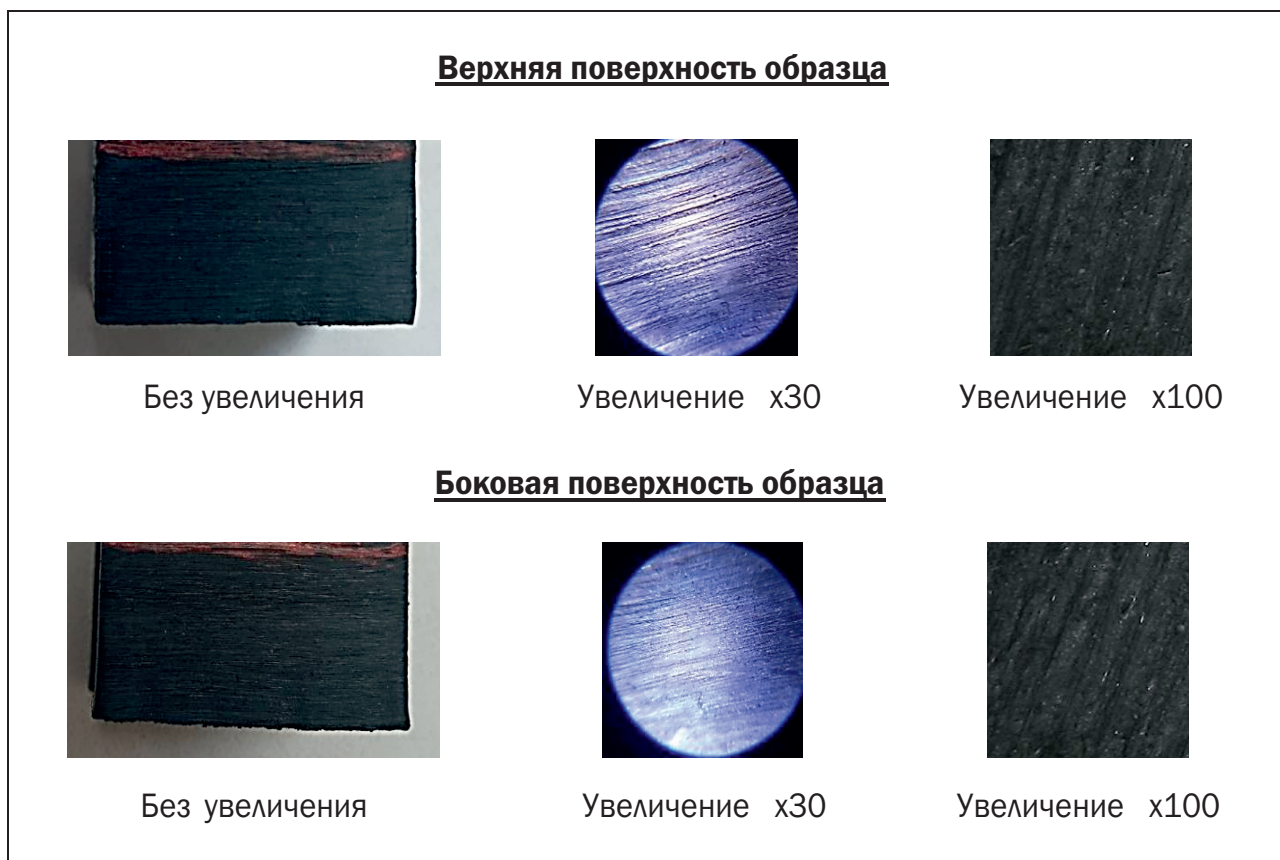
Часть заготовки, обработанная абразивным кругом мелкой зернистости
